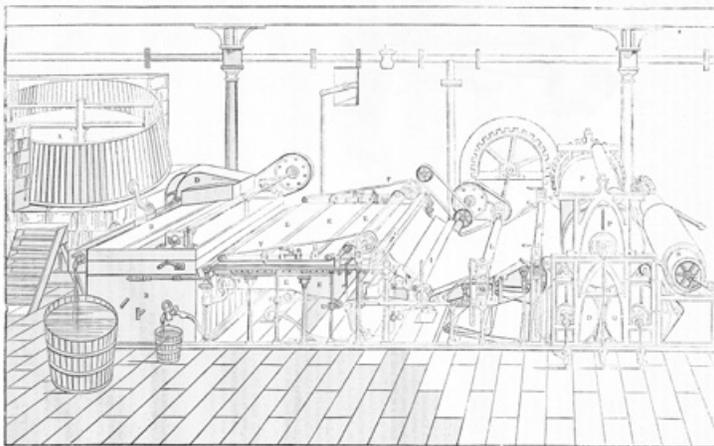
Machine à fabriquer le papier, Extrait de la revue *Magasin pittoresque*, Paris, 1834
